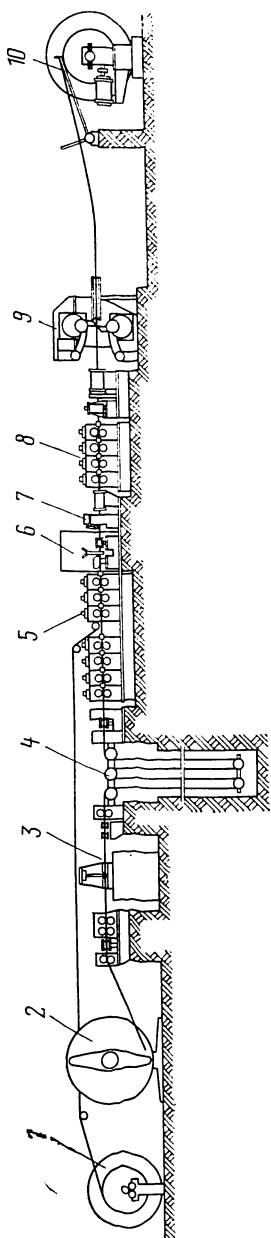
Схема агрегата для высокочастотной сварки оболочек.
